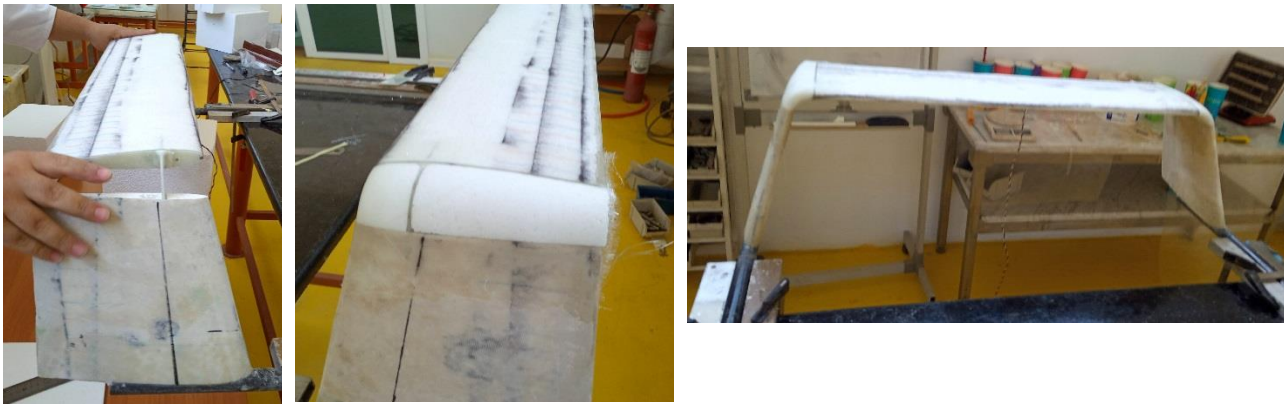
Fixation des empennages verticale sous l'empennage horizontal
